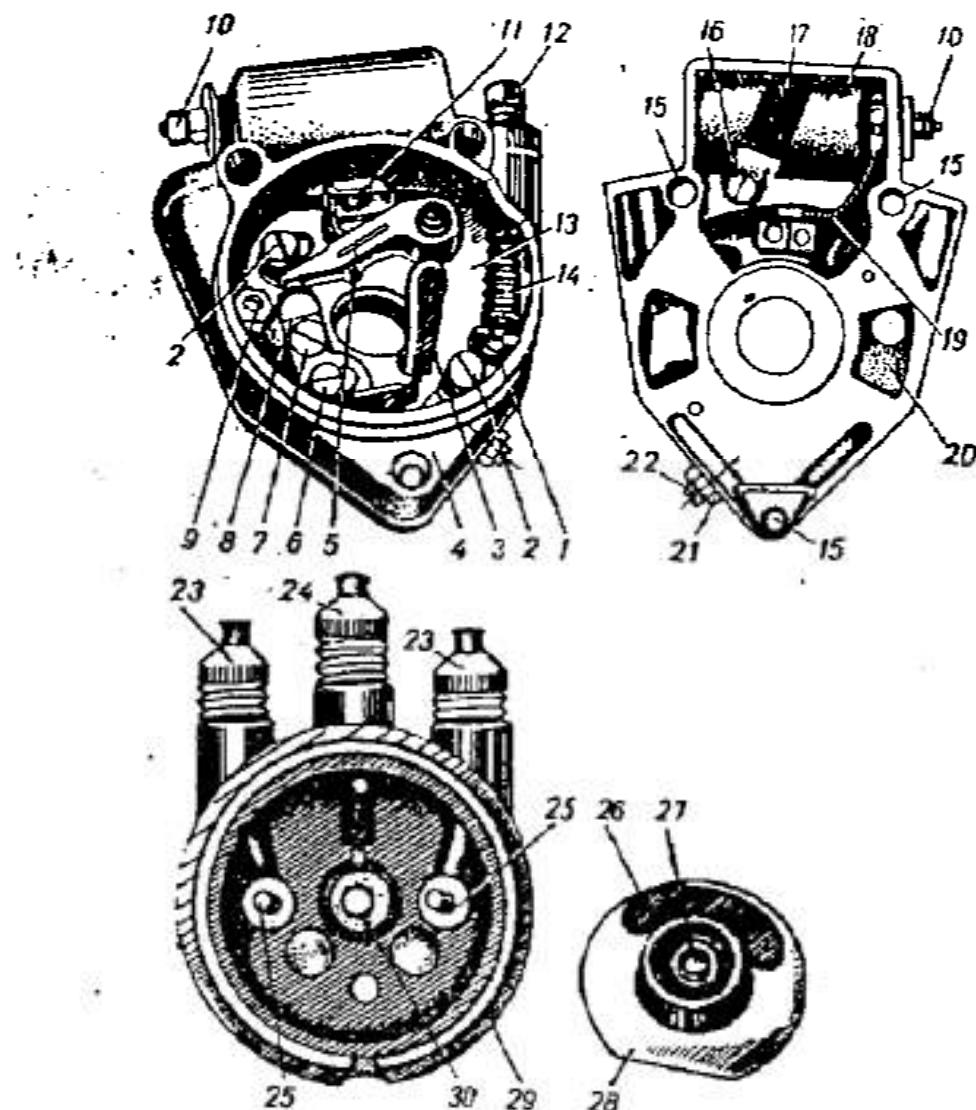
Устройство прерывателя-распределителя ИМ-05.
